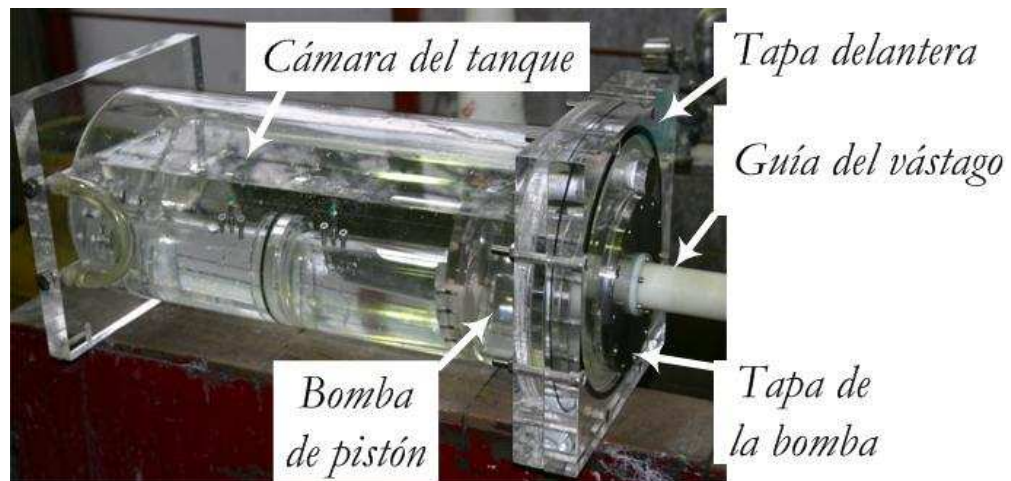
Estado final de la manufactura y ensamble del tanque.
